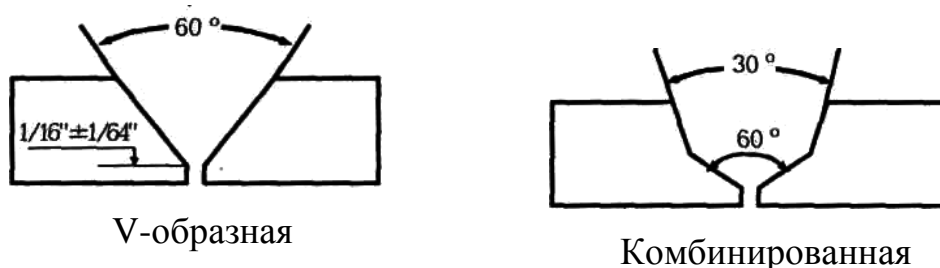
Разделка кромок для сварки процессом STT [9]
